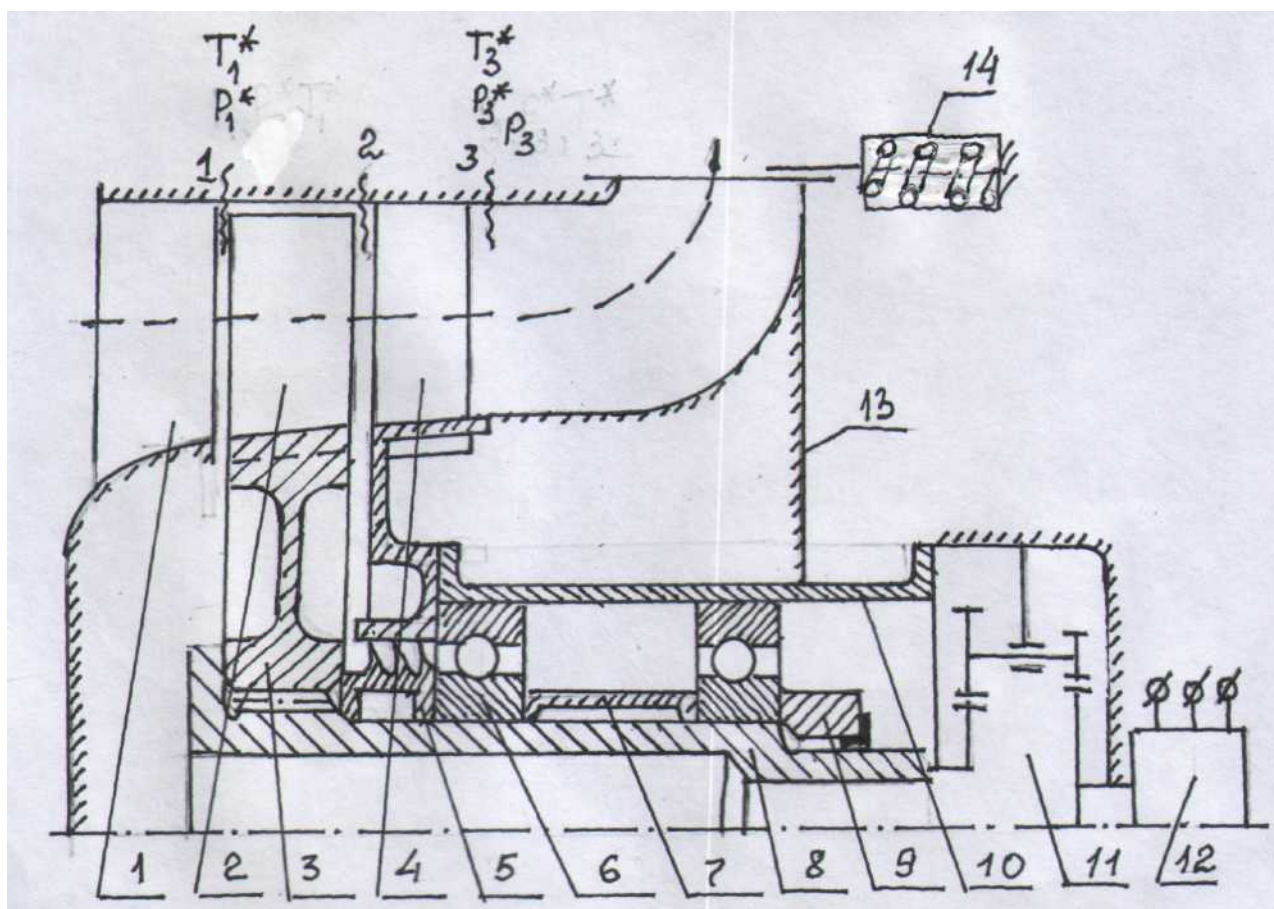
Конструктивно-компоновочная схема лабораторной установки для исследования рабочего процесса в осевой ступени компрессора:
